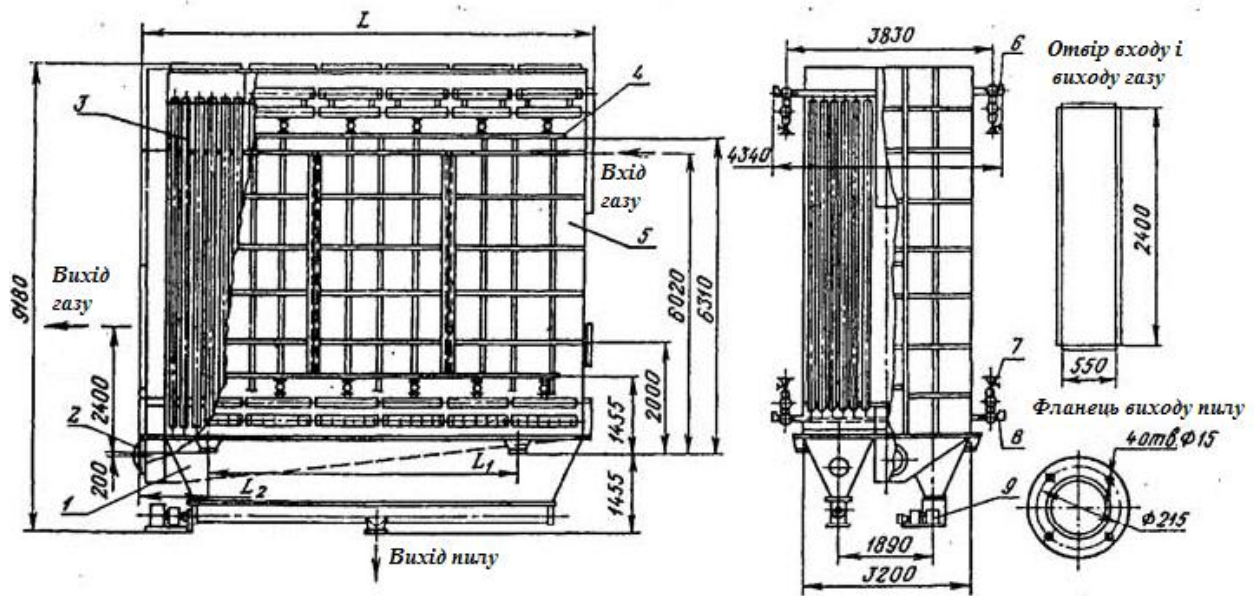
Рукавні фільтри типу ФРКДІ: 1 – бункерна частина корпусу; 2 – люк; 3 – рукав; 4 – колектор; 5- корпус; 6 – секція клапанів; 7 – фланцевий вентилятор; 8 – секція клапанів; 9 – гвинтовий транспортер.
